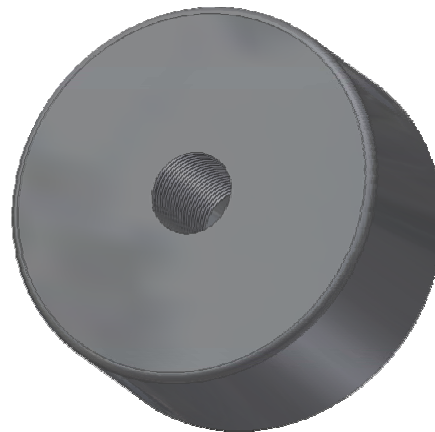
51. Pistón en detalle. Fuente: Los Autores.
